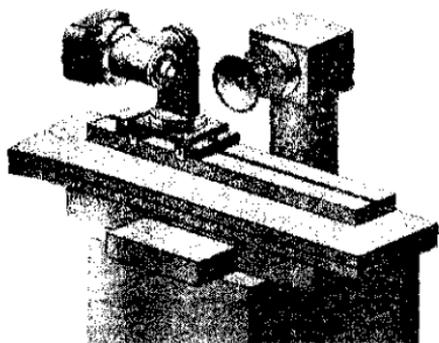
Широкоуниверсальный заточный станок с предлагаемым приспособлением
